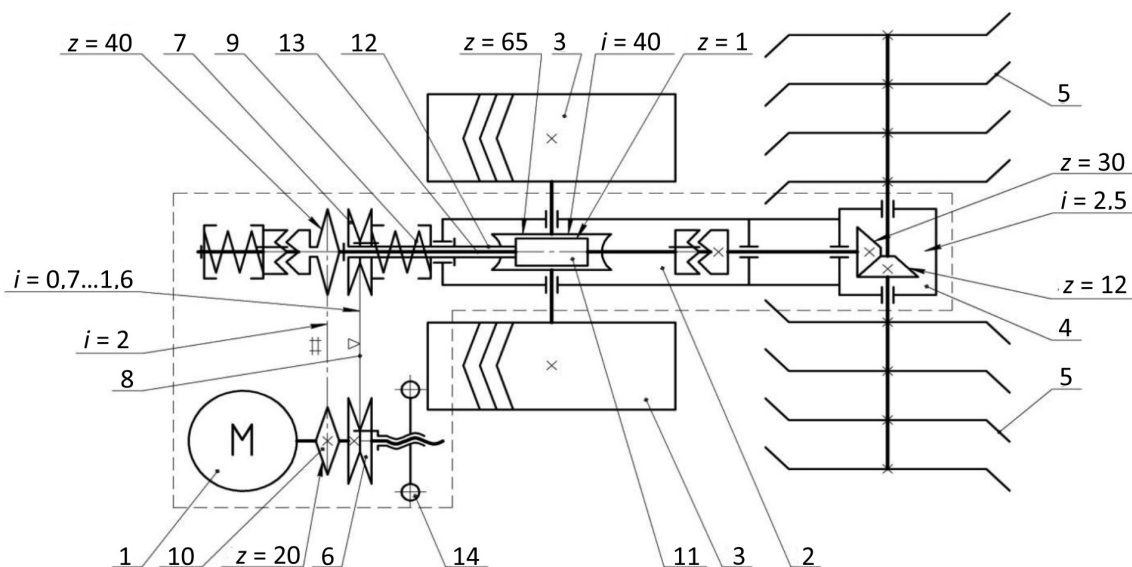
Кинематическая схема опытного образца СМПФ ФС-0,85: 1 – электрический двигатель; 2 – редуктор привода ходовой части; 3 – ходовые колеса; 4 – привод рабочих органов; 5 – фрезерные рабочие органы; 6 и 7 – ведущий и ведомый шкивы вариатора; 8 – клиновой ремень; 9 – пружина ведомого шкива; 10 – звездочка; 11 – червяк; 12 – полый вал; 13 – центральный вал; 14 – маховик управления клиноременным вариатором
